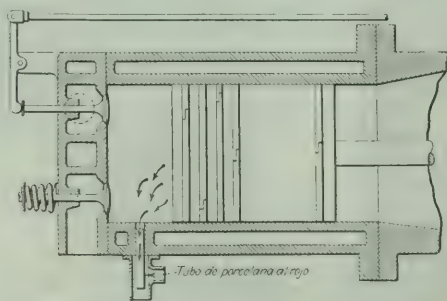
TUBO CALIENTE DE IGNICIÓN PRIMITIVO
